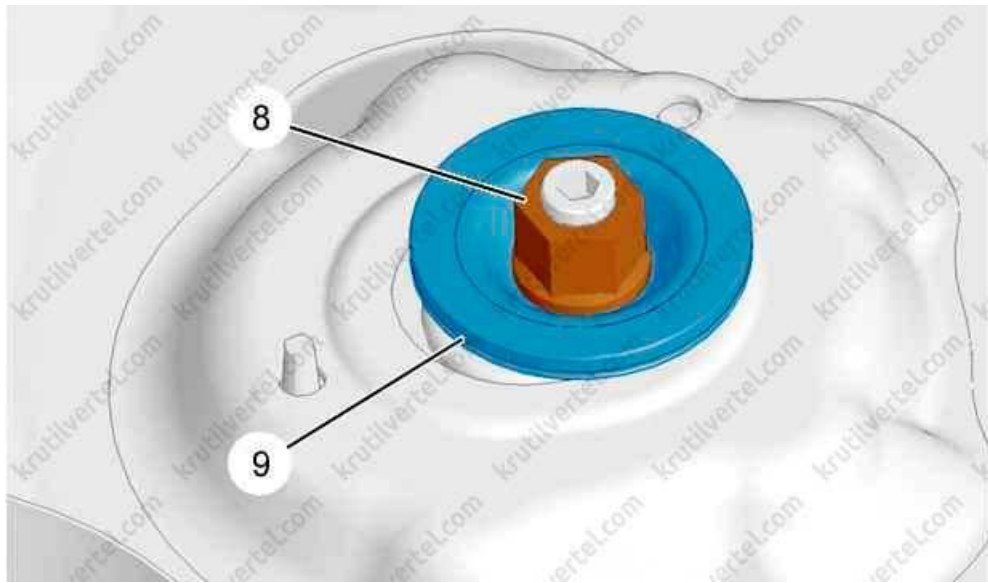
Демонтаж верхнього кріплення стійки:
